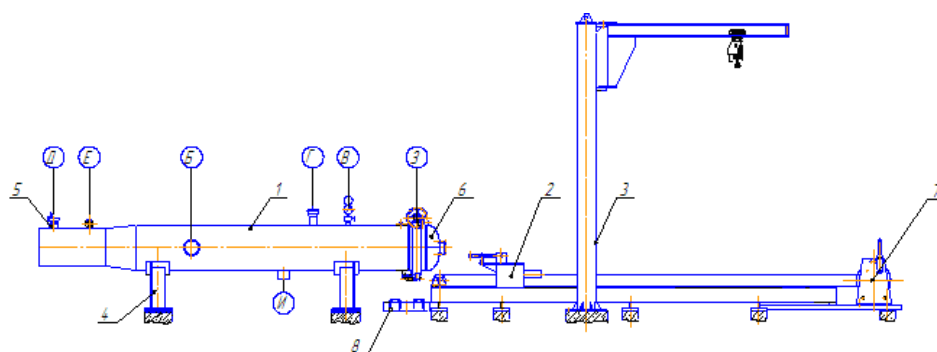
Устройство камеры приема. 1 – корпус камеры приема;
